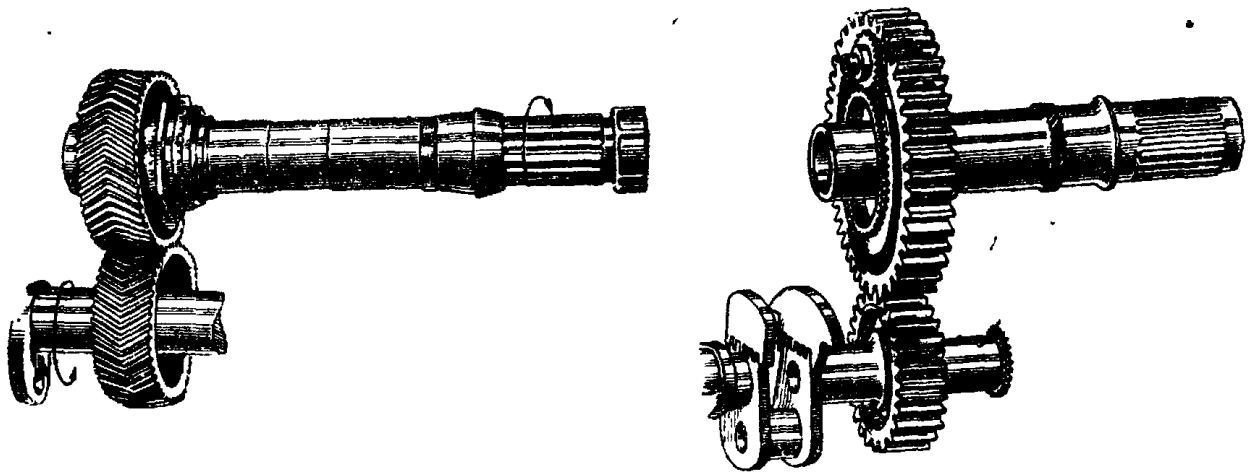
Редуктори рядних двигунів з циліндричними шестернями
